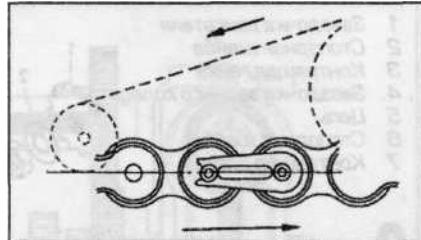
г Пружинный замок следует устанавливать таким образом, чтобы его неразъемная часть смотрела по направлению движения цепи
